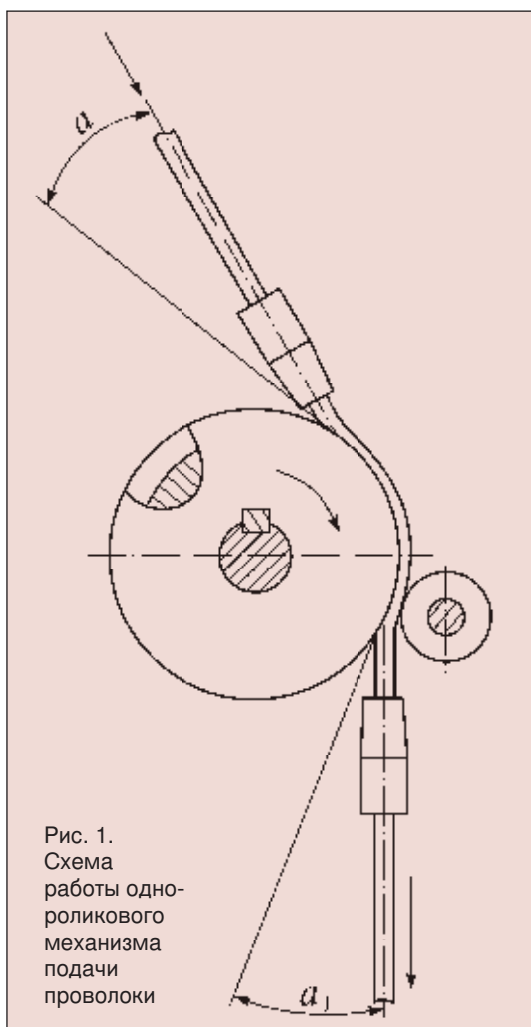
Схема работы одно-роликового механизма подачи проволоки
